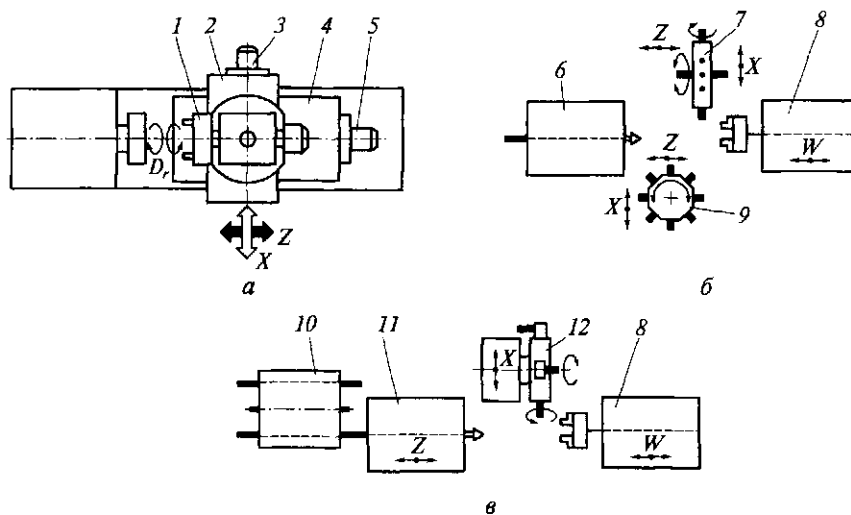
Компоновки МС для обработки деталей типа тел вращения на базе токарного станка (а), токарно-револьверного станка (б) и одношпиндельного токарно-револьверного автомата (в):
